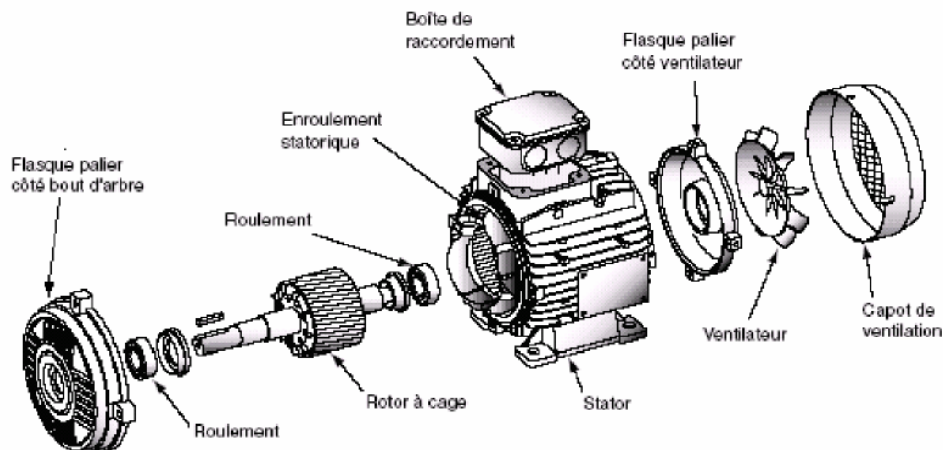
Vue générale d'une machine asynchrone triphasée à cage
